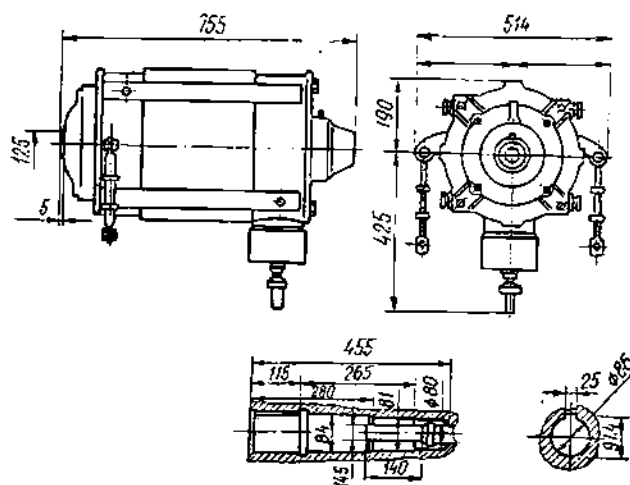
Dimensiunile de gabarit și montaj ale motorului RTF-12 S.
